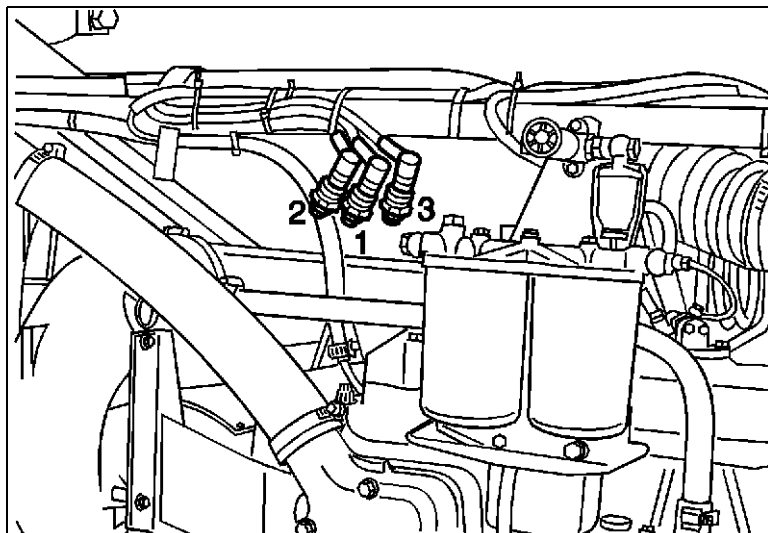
Interruptor para arranque y parada del motor Verde - interruptor de arranque.
